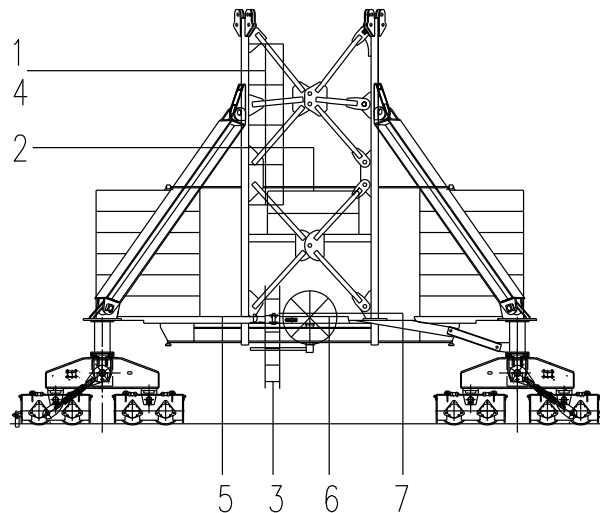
安装底盘通道 Fig. 4-8 Fitting Chassis Access
